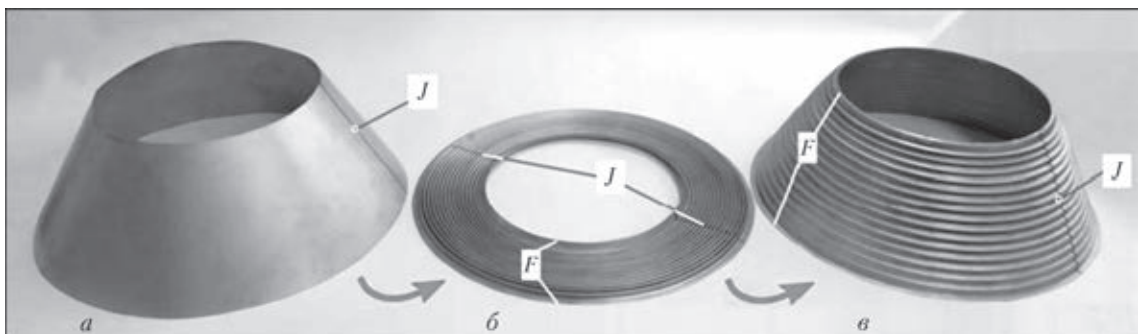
Стадии изготовления преобразуемой конической оболочки КПО, иллюстрирующие характер технологического деформирования ее сварных соединений  $J$  ( $F$  — фланцевая отбортовка для последующей сварки оболочек в единую структуру)
